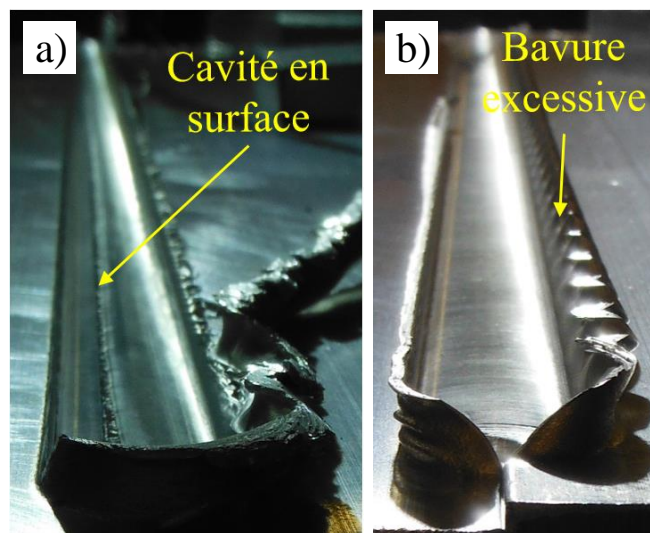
Conditions de surface des soudures a) M10AS01 b) M10RS01
